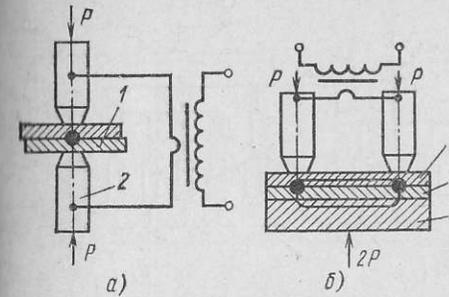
Схема контактной точечной сварки: а — двусторонней; б — односторонней
